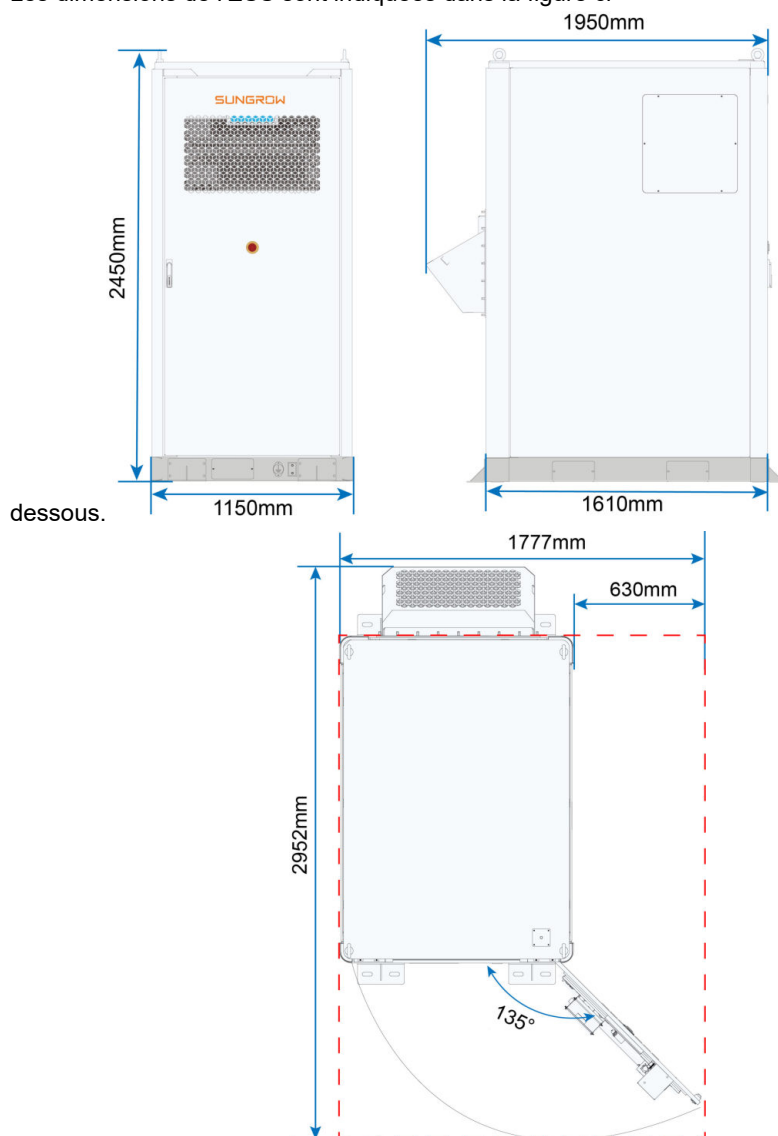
Dimensions de l'ESS avec sa porte complètement ouverte
